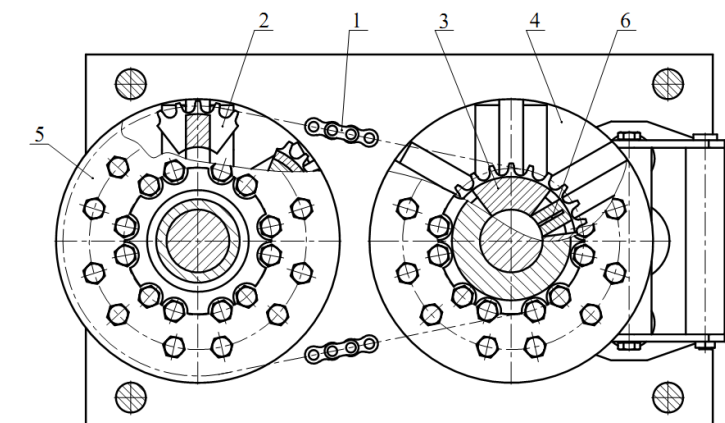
Вариатор с приводной роликовой цепью: 1 – приводная роликовая цепь; 2 – зубчатый сектор ведомой звездочки; 3 – зубчатый сектор ведущей звездочки; 4 – составная ведущая звездочка; 5 – составная ведомая звездочка; 6 – пластинчатая пружина
